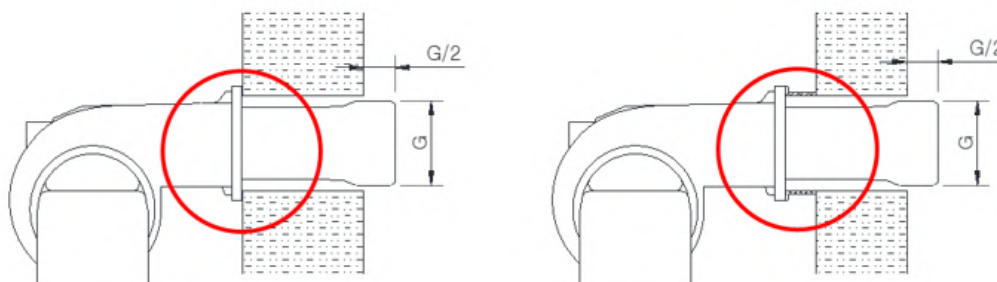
F-C. Instalação Incorreta do Queimador Padrão]
